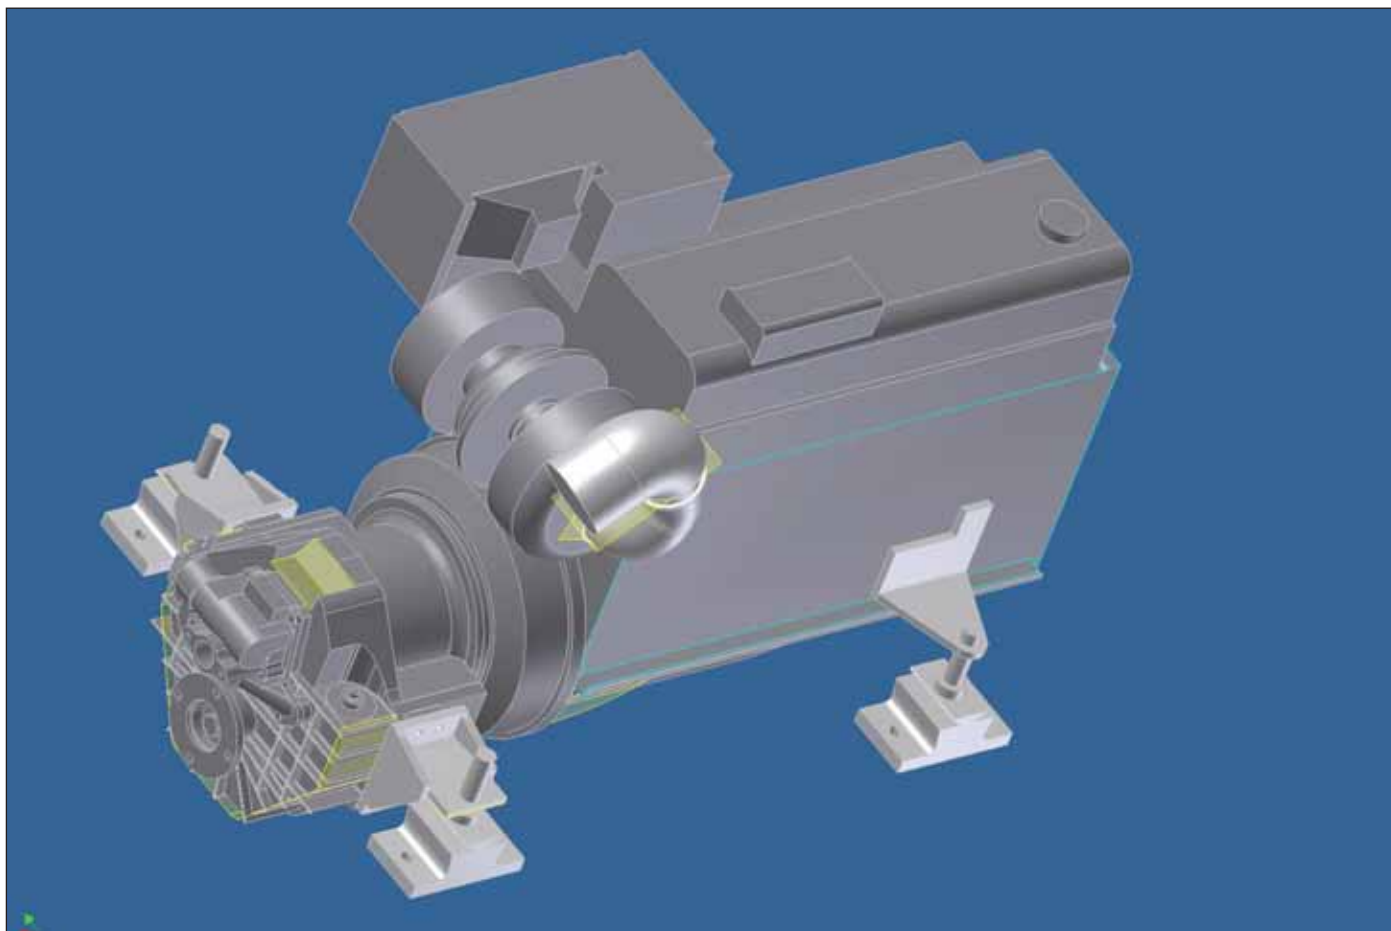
Главный двигатель "Yanmar 6LPA-STP" с редуктором
